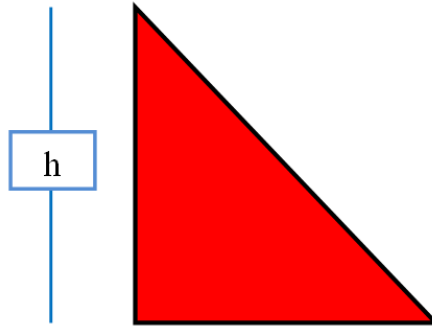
Vista de cordón de soldadura en 2D.
